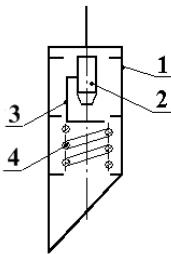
Схема ДП: 1 – корпус; 2 – сопло; 3 – ковадло; 4 – пружина.
